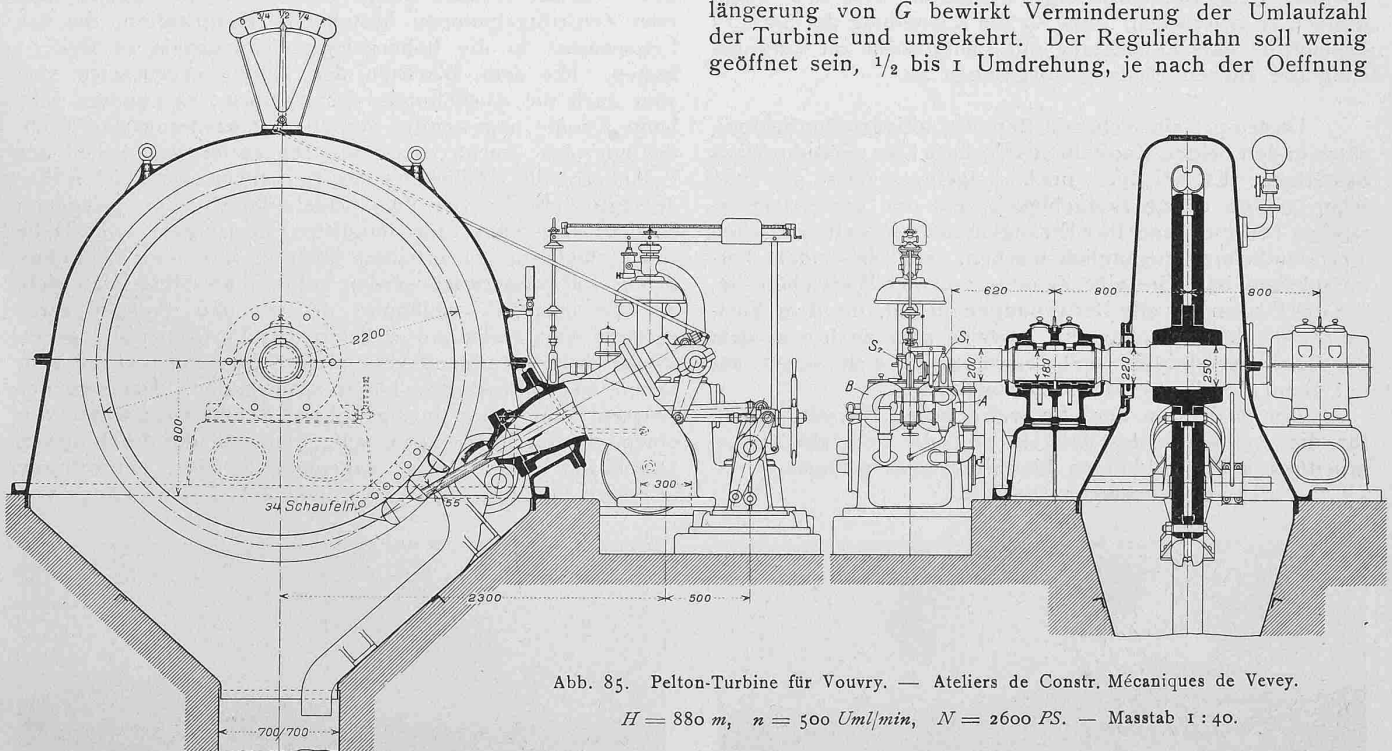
Pelton-Turbine für Vouvy. — Ateliers de Constr. Mécaniques de Vevey.
